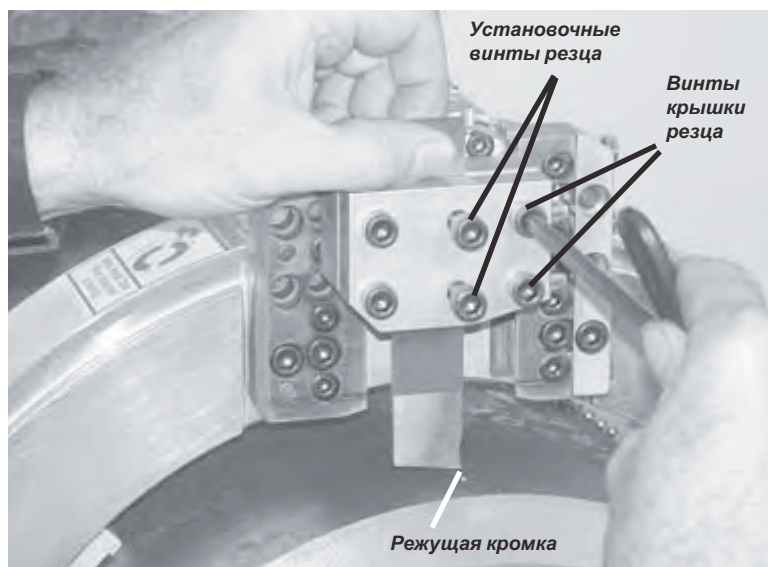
Установка отрезного резца режущей кромкой в указанном направлении резания.
